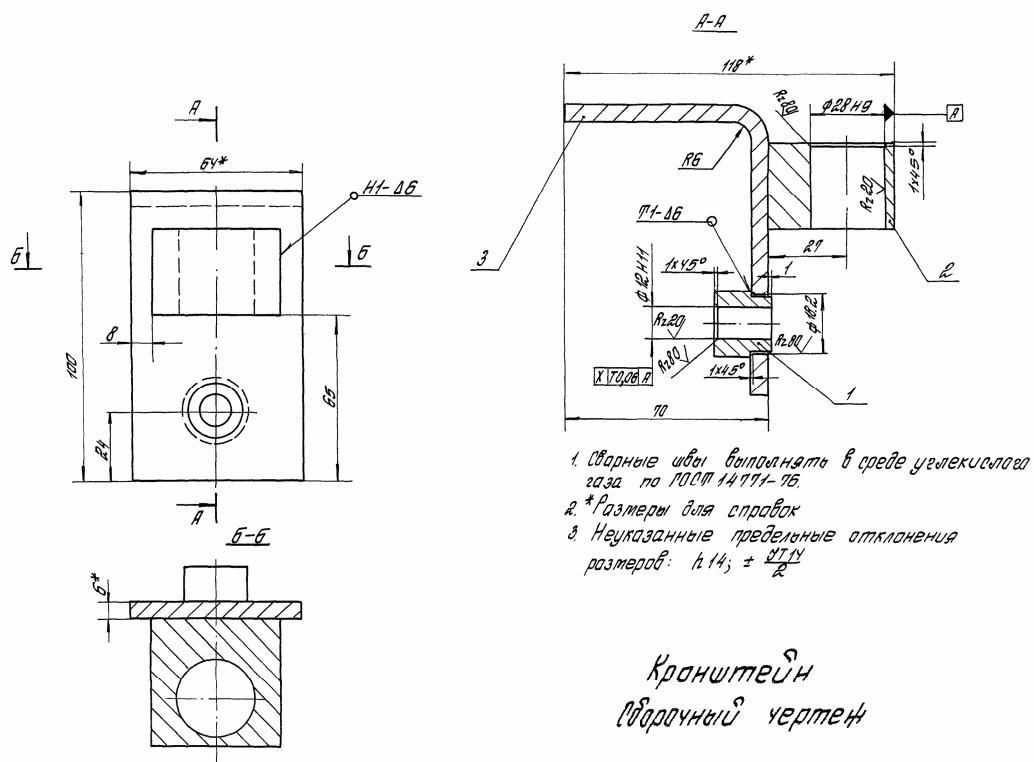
Пример чертежа сборочной единицы, полученной сваркой
